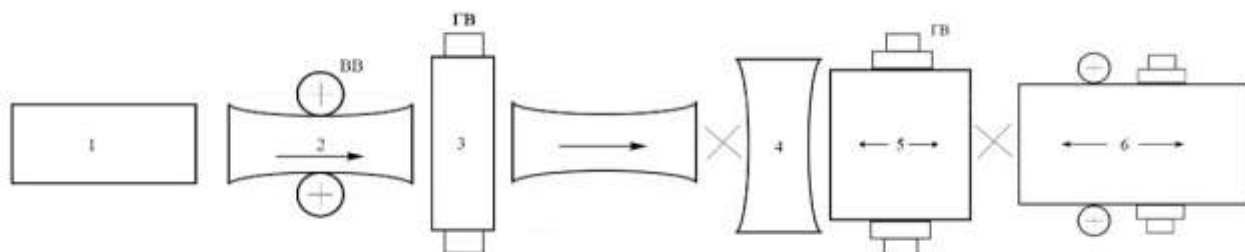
Схема прокатки толстых листов с обжатыми кромками:
